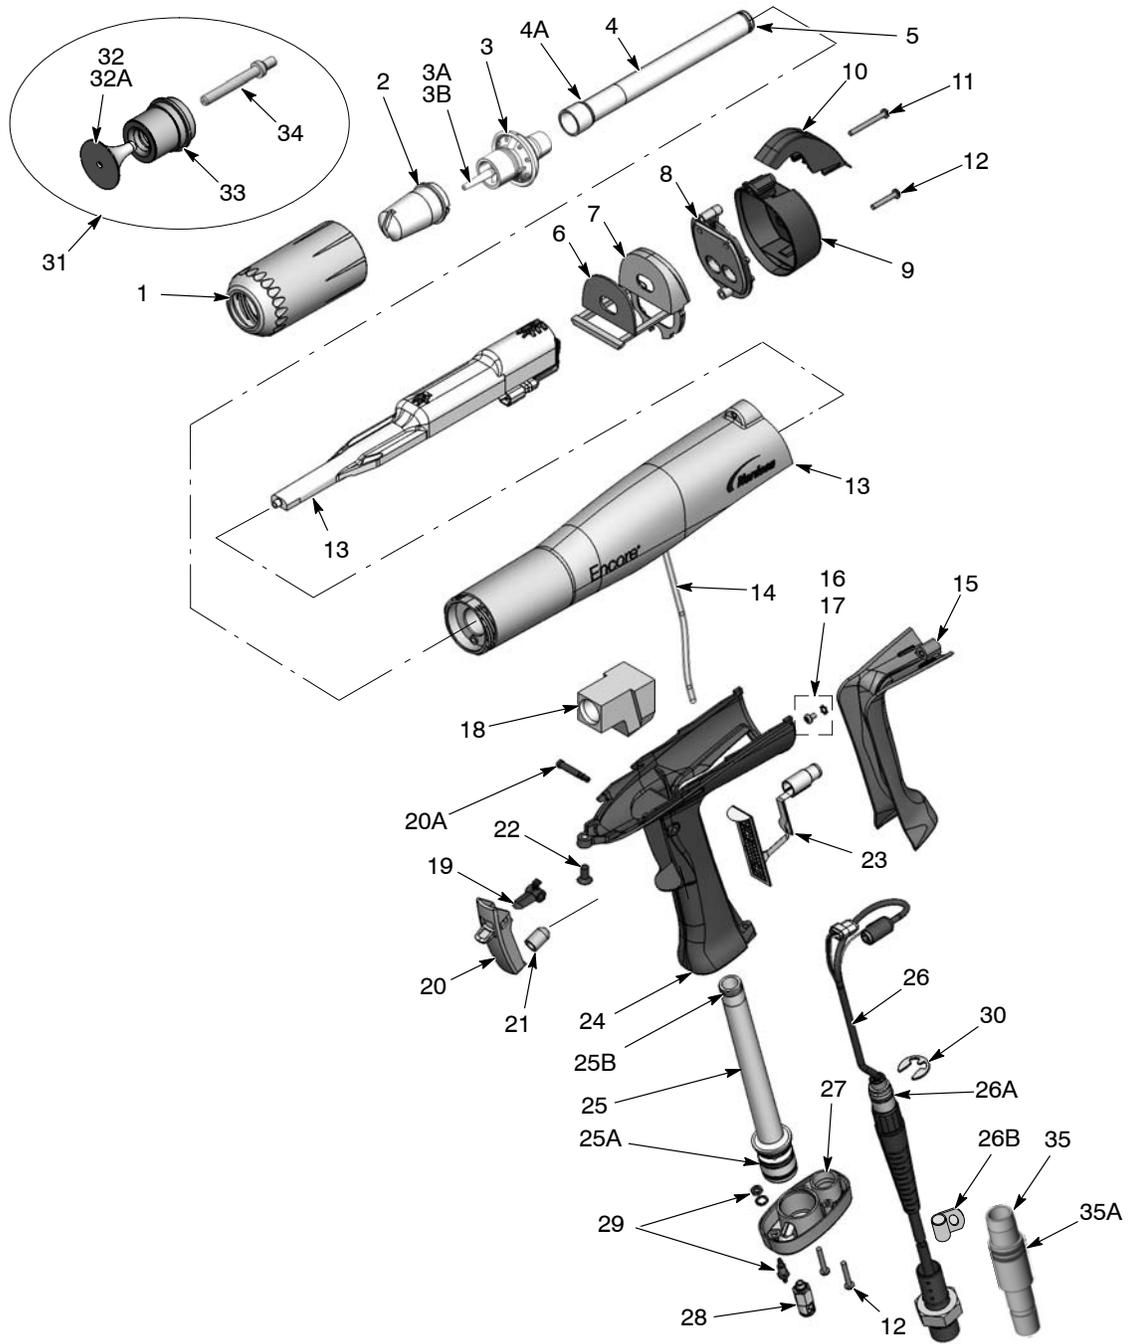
Вид с разделением деталей ручного распылителя Encore и принадлежностей
